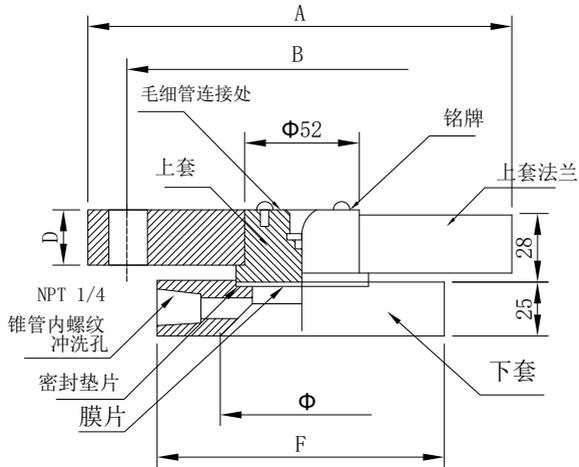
RFW 型法兰安装远传装置外形尺寸图
